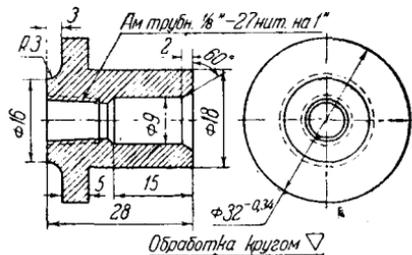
Дет. № 18-29. Втулка смазочного шланга
